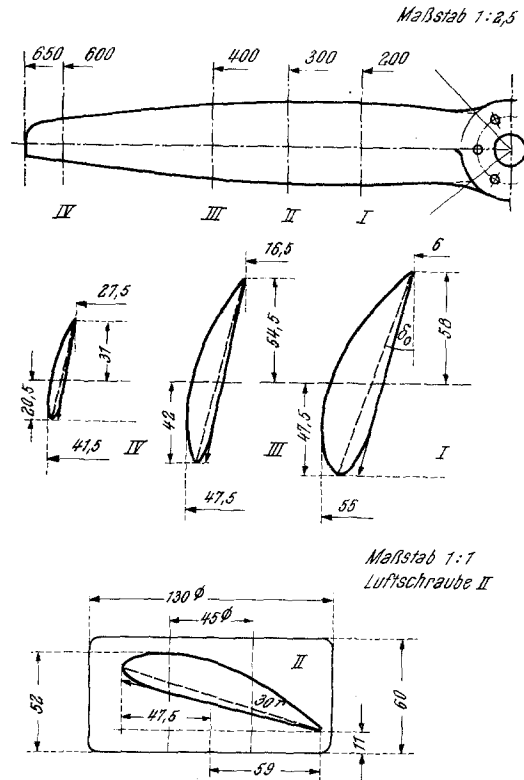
Auszug aus der Konstruktionszeichnung einer der beiden untersuchten Luftschrauben
